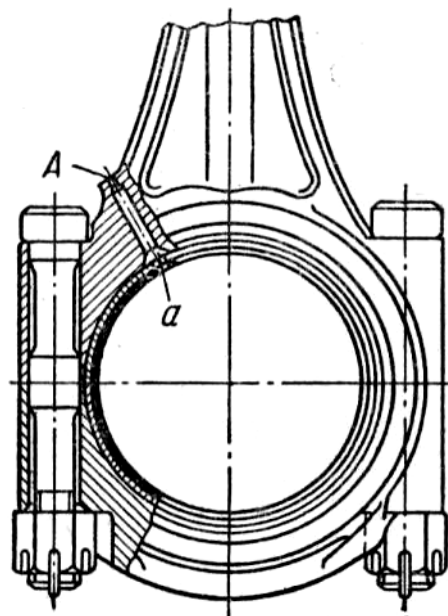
Конструктивне оформлення кривошипної головки шатуна
